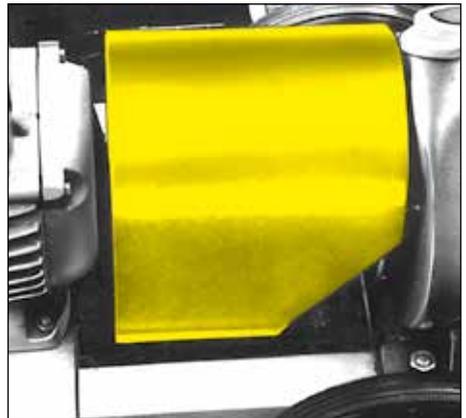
Wellen sind zu verkleiden. Dies gilt auch für Antriebswellen, die unter Fahrzeugen und Arbeitsmaschinen liegen.
